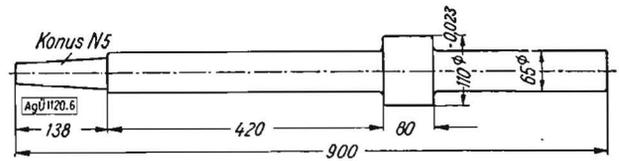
Bohrstange zum Ausbohren der Zylinderblockbuchsen von Motoren der Traktoren S-80 und S-65
